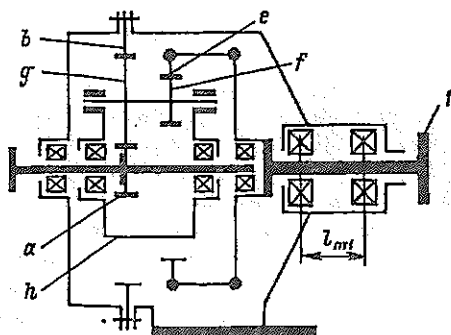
Компоновочная схема редуктора по схеме $3k$
